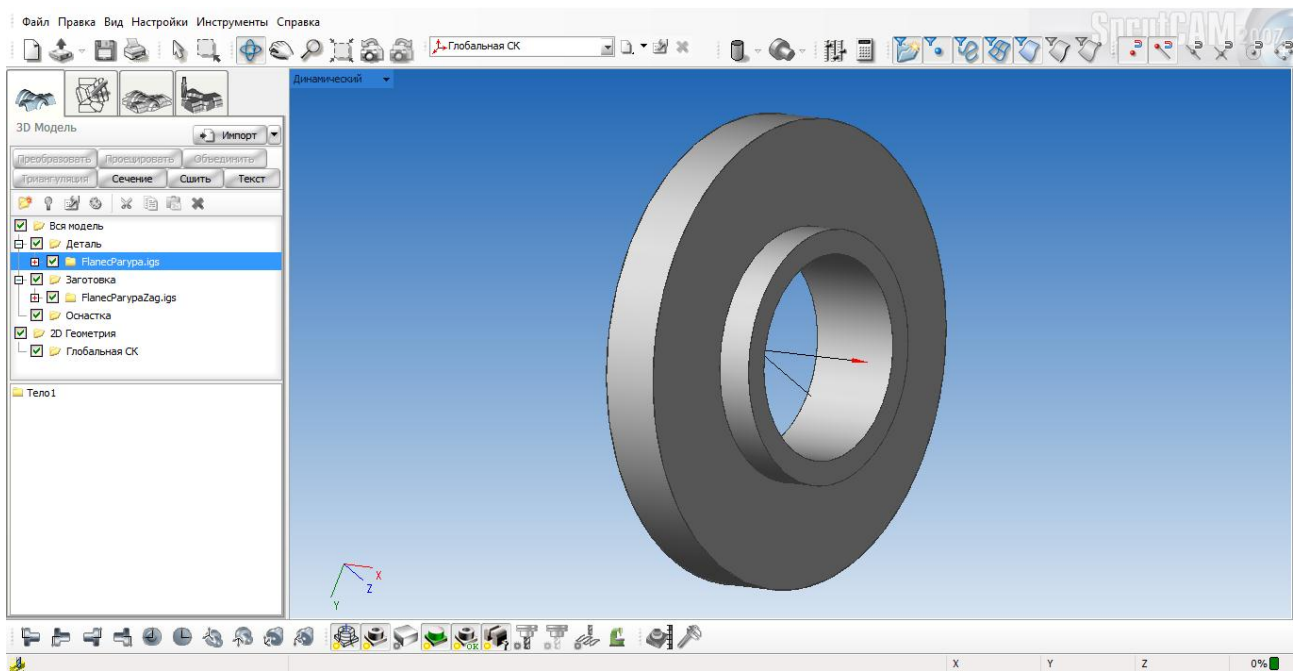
3D-моделі деталі та заготовки після імпорту в систему Sprut-CAM
